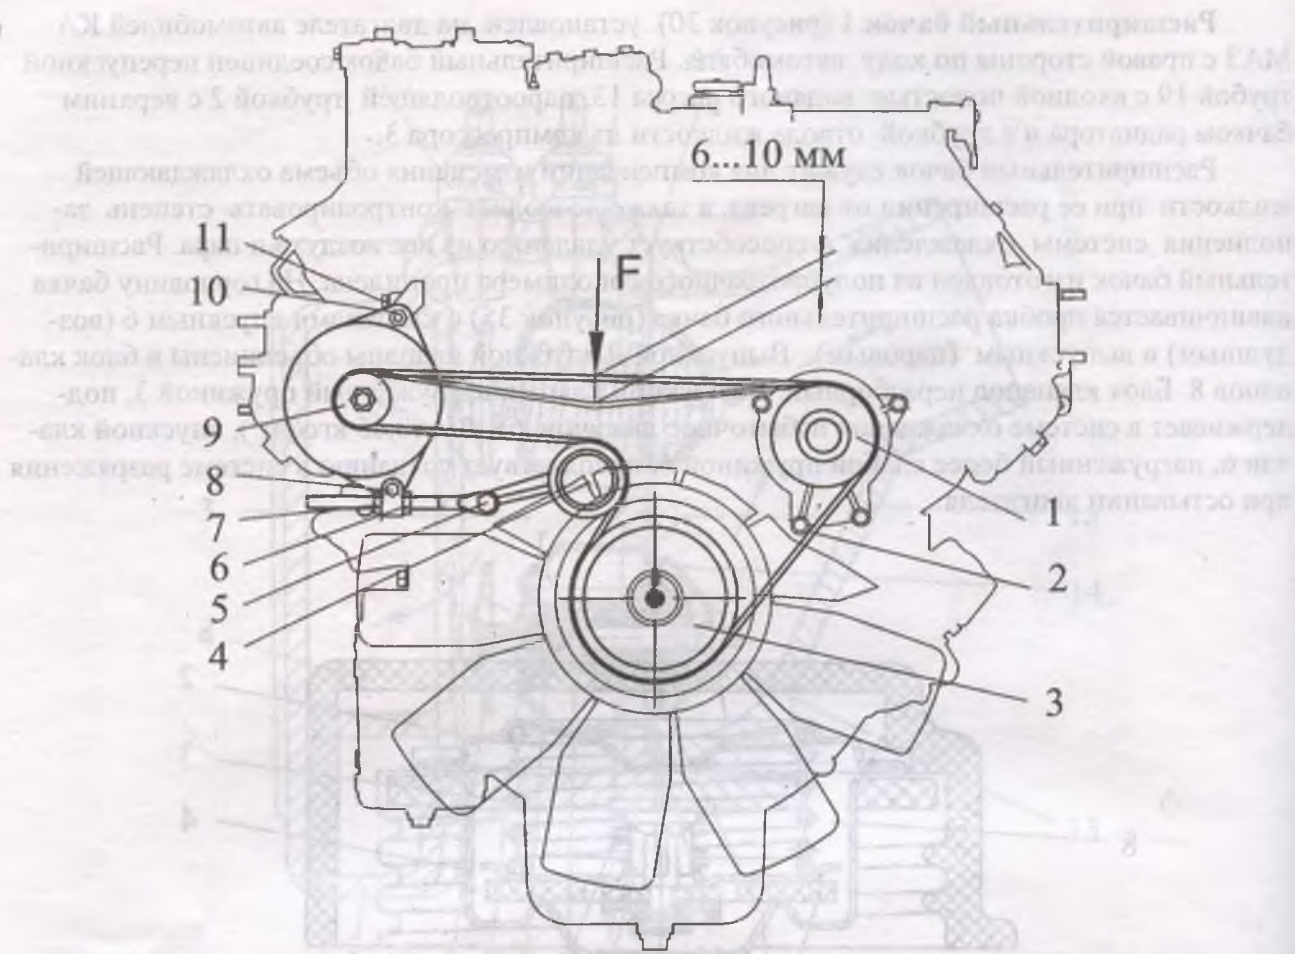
схема проверки натяжения ремней привода генератора и водяного насоса с расположением вентилятора по оси коленвала:
